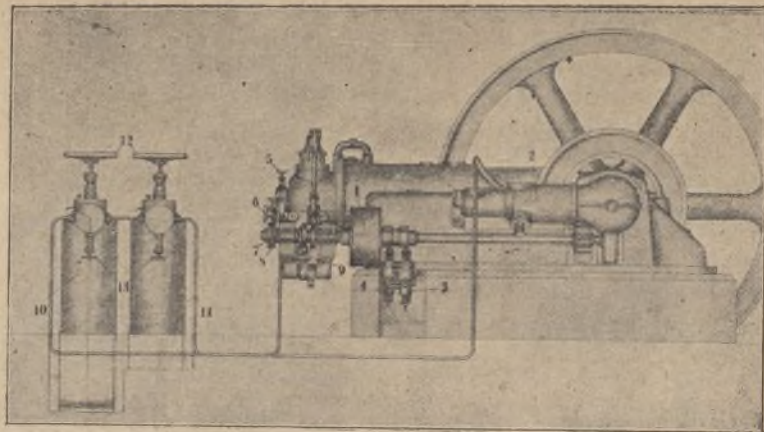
Vista del motor de combustión interna, sistema Dingler.
